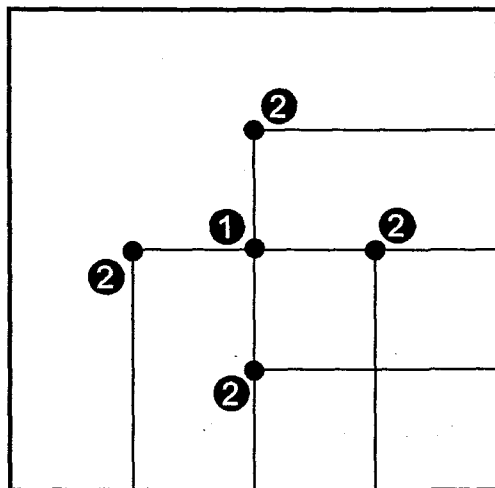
Схема отбора проб с катаной заготовки сечением 125x125 мм
